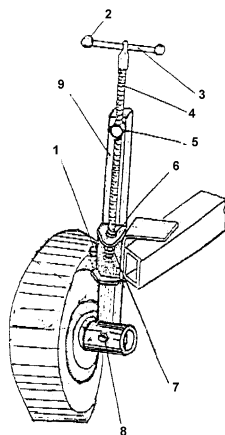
Сборка заднего колеса с механизмом регулировки ПКГ 06.000
